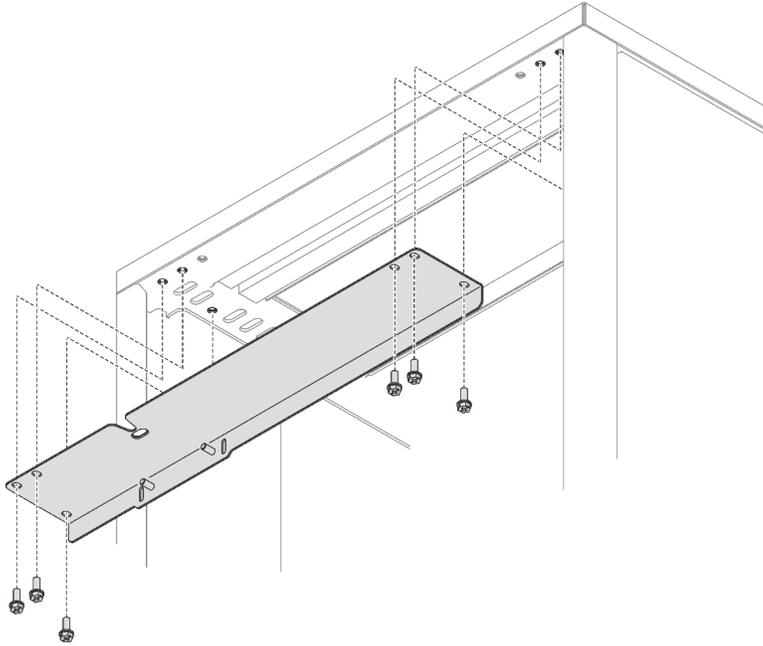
Entfernen der obere Montagehalterung für die Rackleitung
